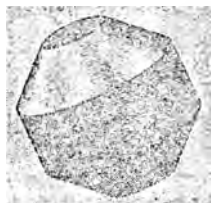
а,б – Заготовка шара, полученная из цилиндра
